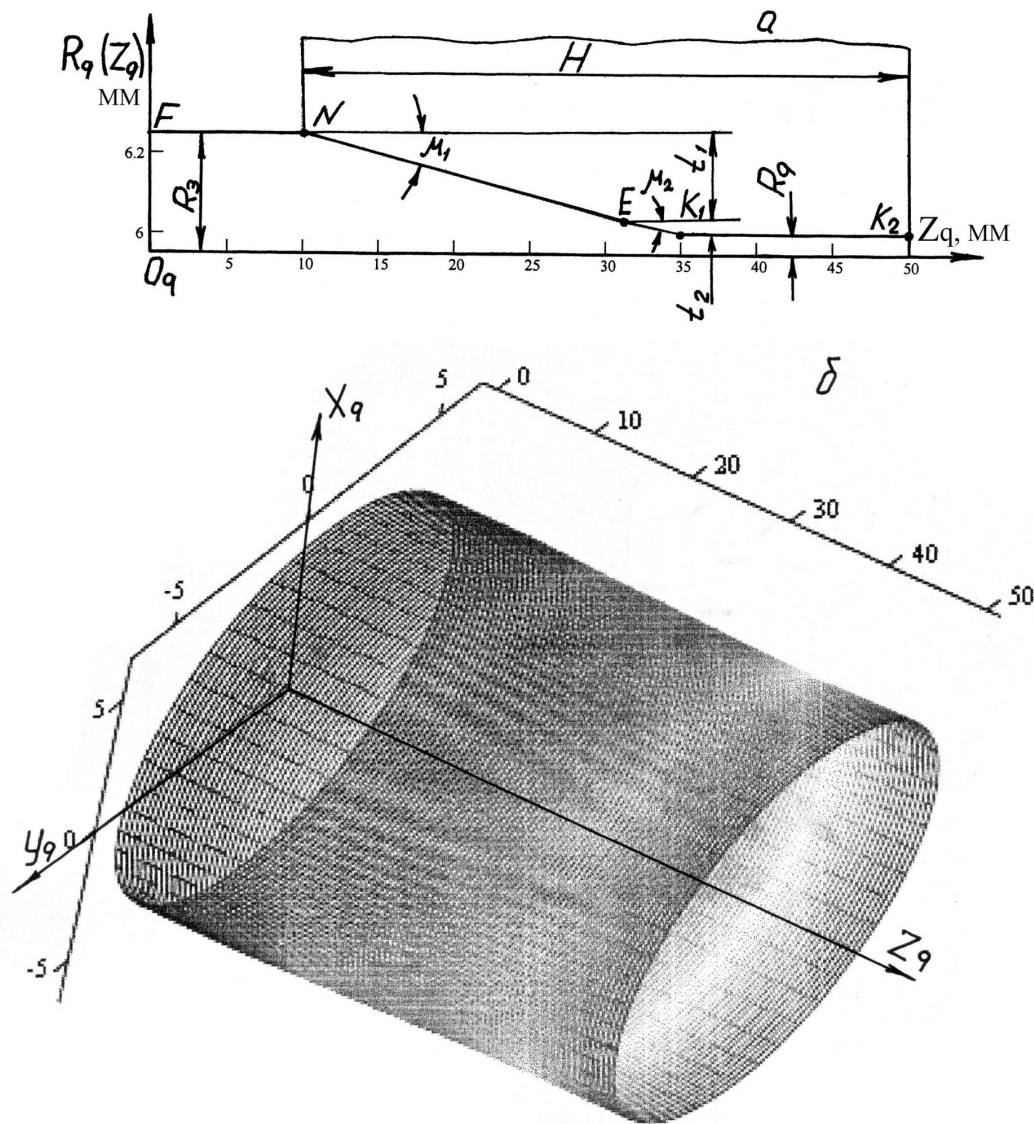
Комбінована поверхня обертання, яка охоплює параметри заготовок і деталей
